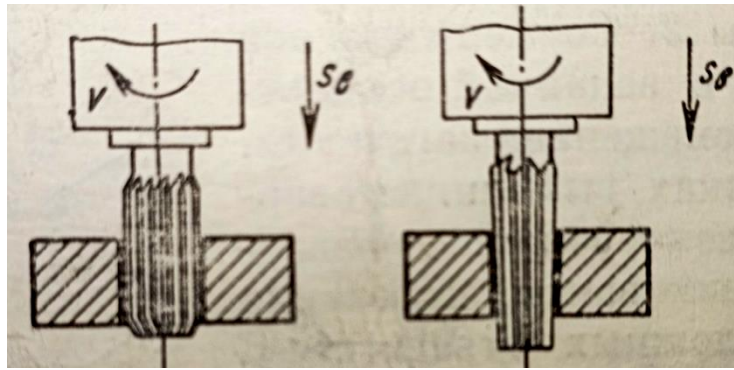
Схема обробки заготовок при виконанні операції розвертування
